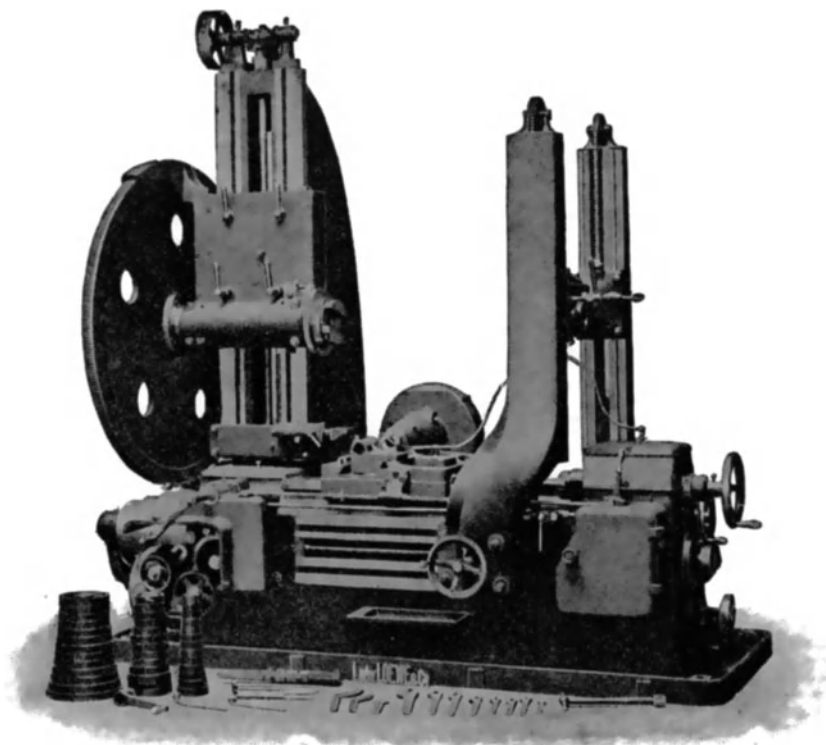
Die selbsttätige Stirnräderfräsmaschine von L. Loewe & Co.
